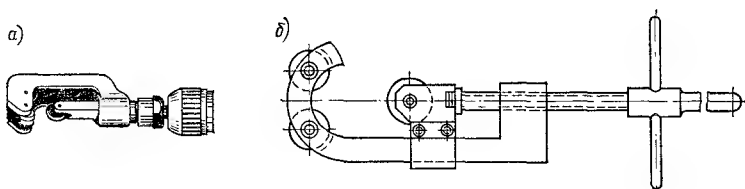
Труборез малогабаритный (а) и роликовый (б)
